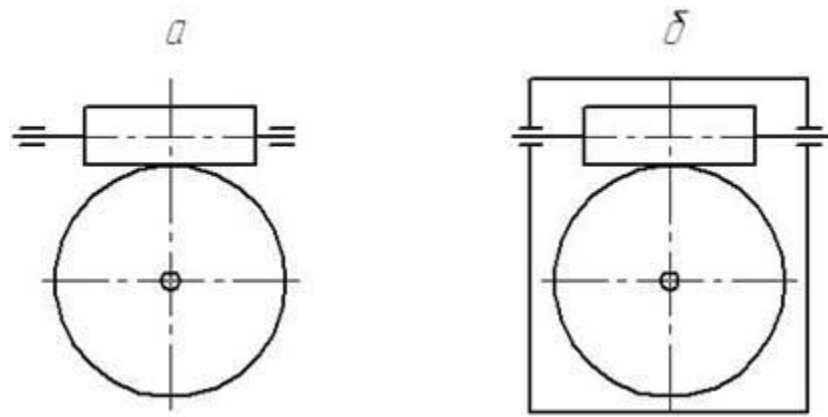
Схеми передавачів за конструкцією корпусу
